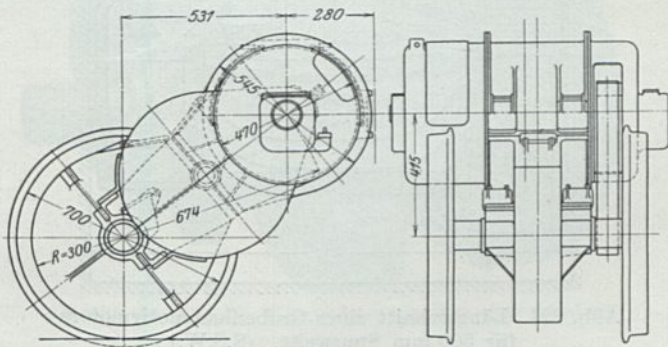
Einbauzeichnung des Motors Abb. 221.
